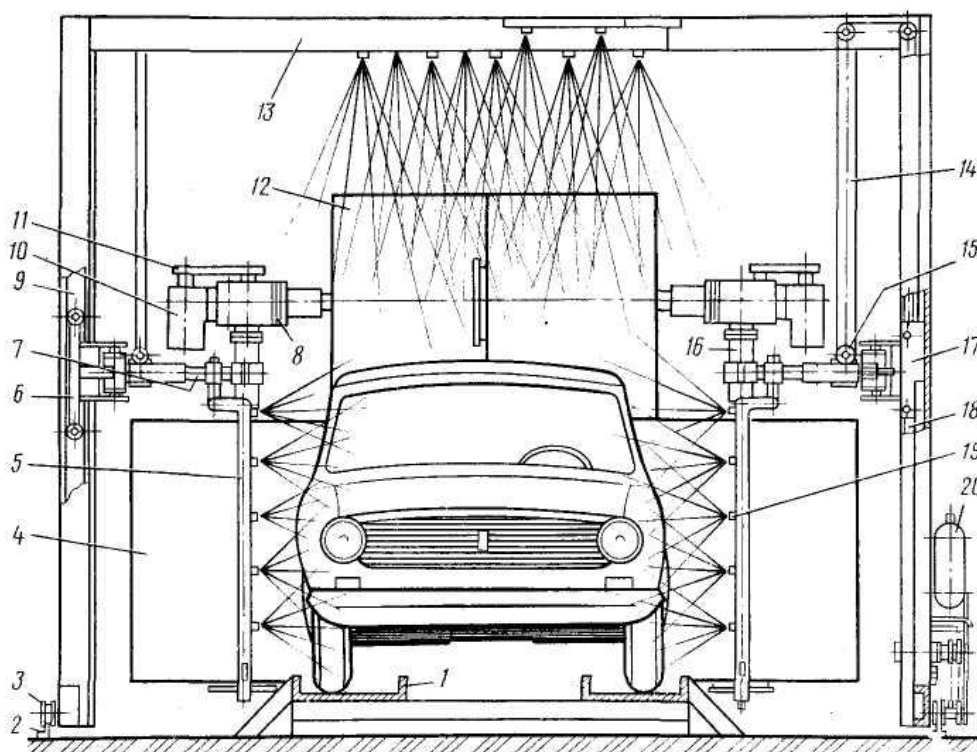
Струйно-щеточная установка для мойки легковых автомобилей:
